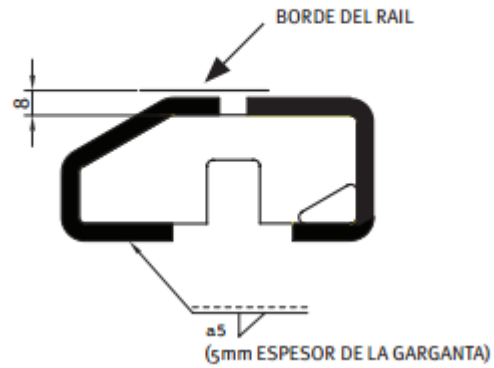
Detalles de soldadura
